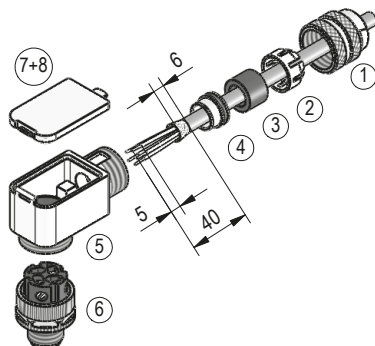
Gegenstecker M12 D-kodiert gewinkelt
